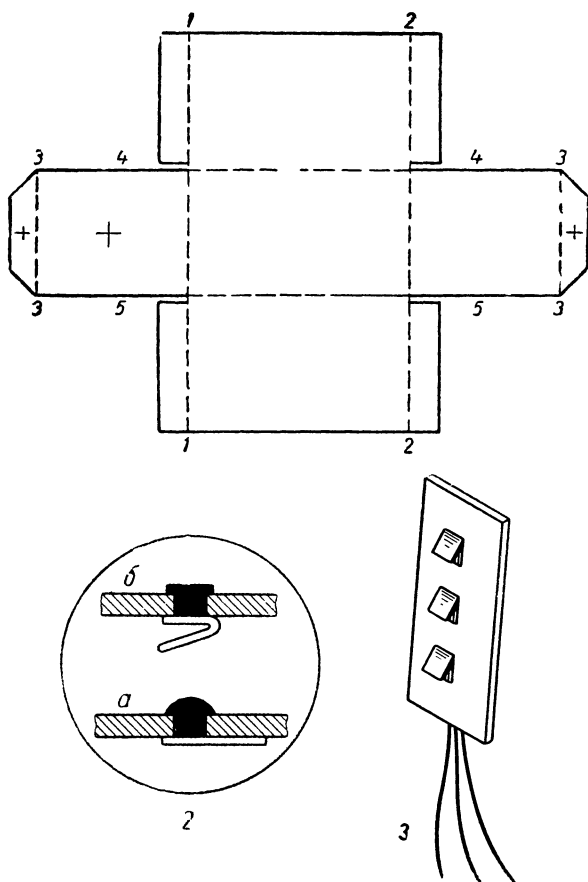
Заготовка для светофорной головки и присоединение проводов.
